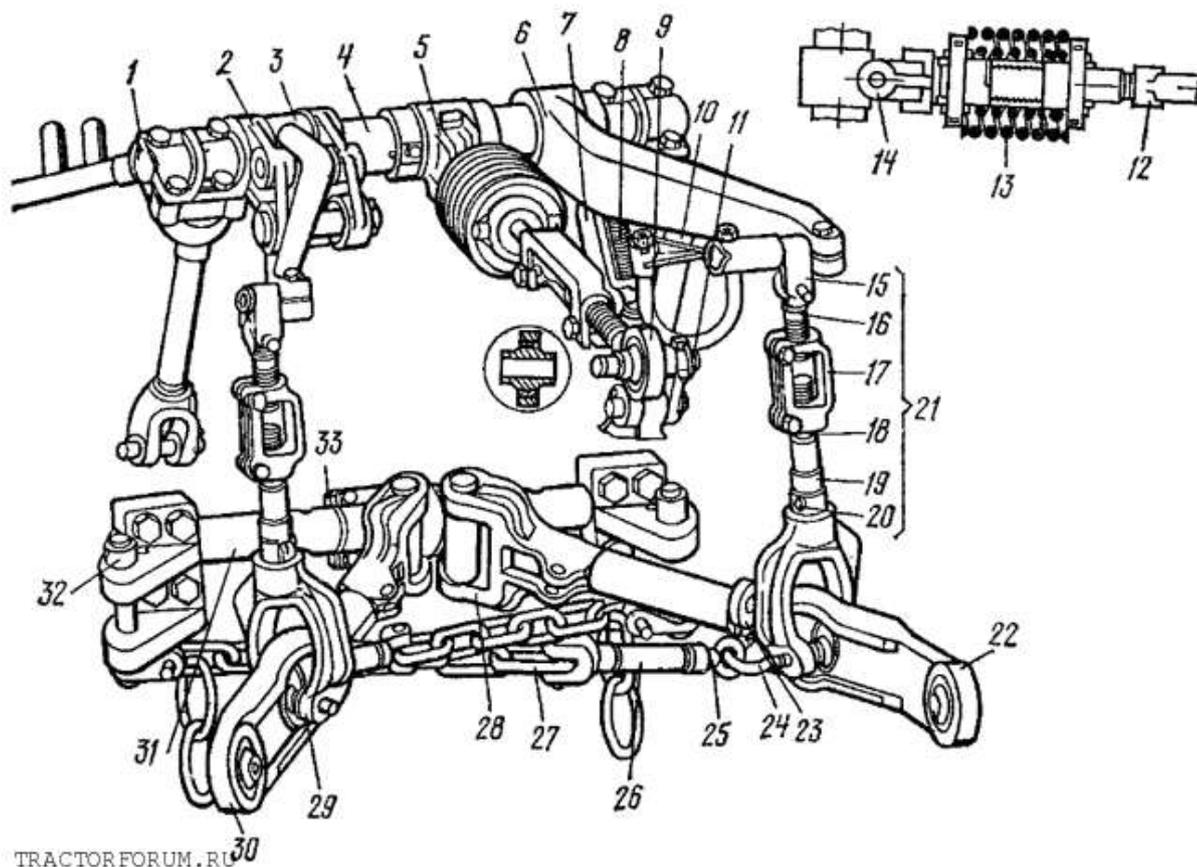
Заднее навесное устройство: 1 — верхняя ось; 2 — рычаг штока; 3 — рычаг левый; 4 — вал; 5 — верхняя тяга; 6 — правый рычаг; 7 и 17 — муфты; 8, 15 и 19 — вилка; 9 — головка верхней тяга; 10 — правая стойка; 11 и 20 — пальцы; 12 — муфта; 13 — пружина; 14 — серьга; 16 — винт; 18 — винт раскоса; 21 — правый раскос; 22 — правая тяга; 23 — рым-болт; 24 — стремянка; 25 — винт растяжки; 26 — муфта растяжки; 27 — цепь; 28 — центральная головка; 29 — левый раскос; 30 — левая тяга; 31 — нижняя ось; 32 — палец прицепной скобы; 33 — упор.
